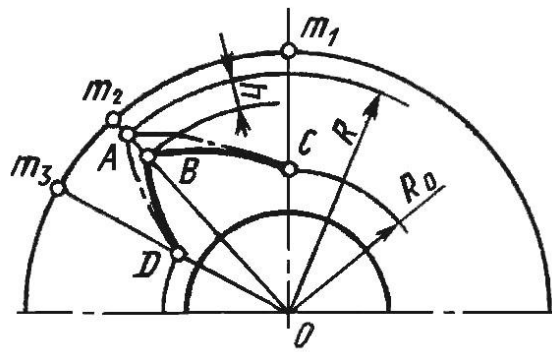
Схема побудови робочої ділянки профілю кулачка для нарізання різі
